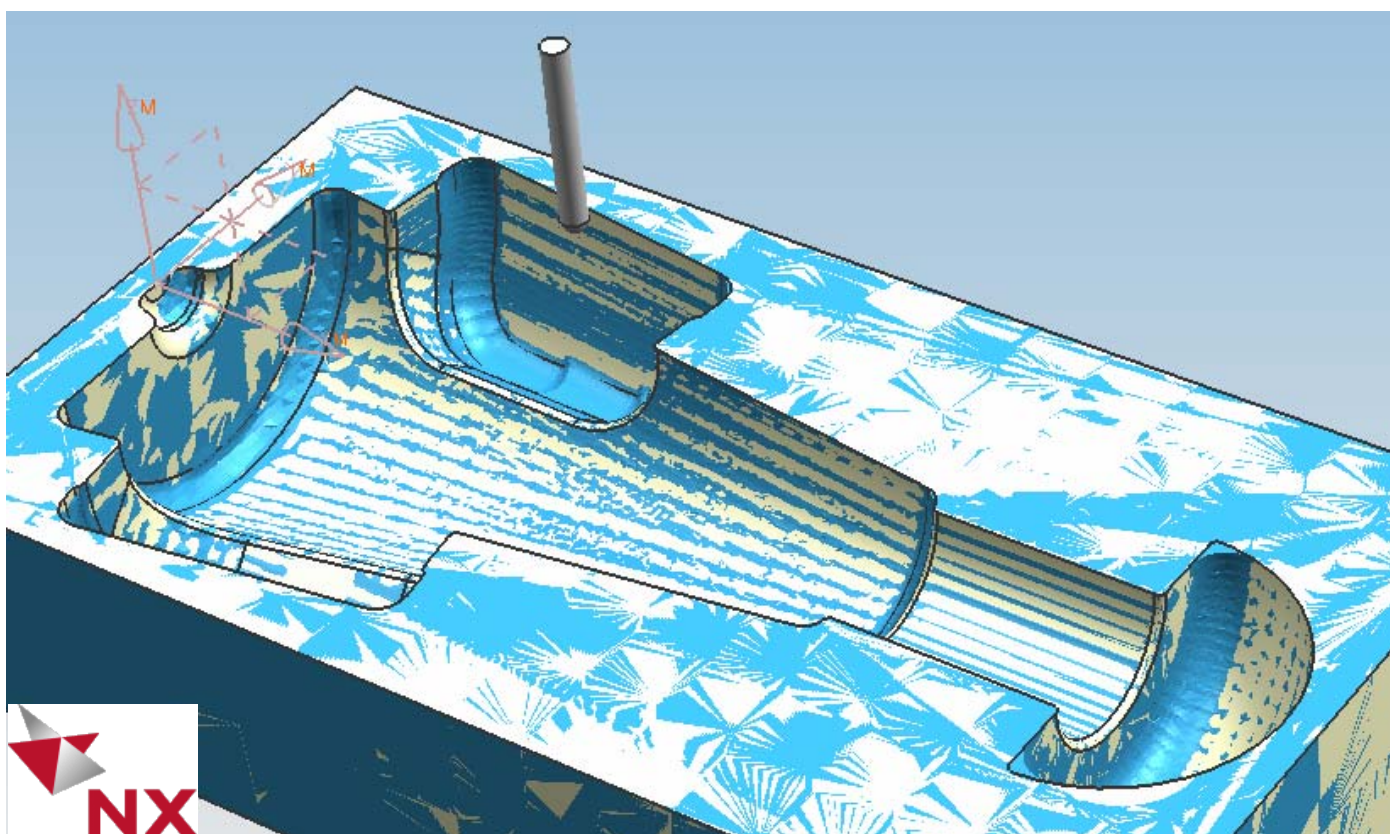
Изготовление стержневого ящика на станке с ЧПУ
